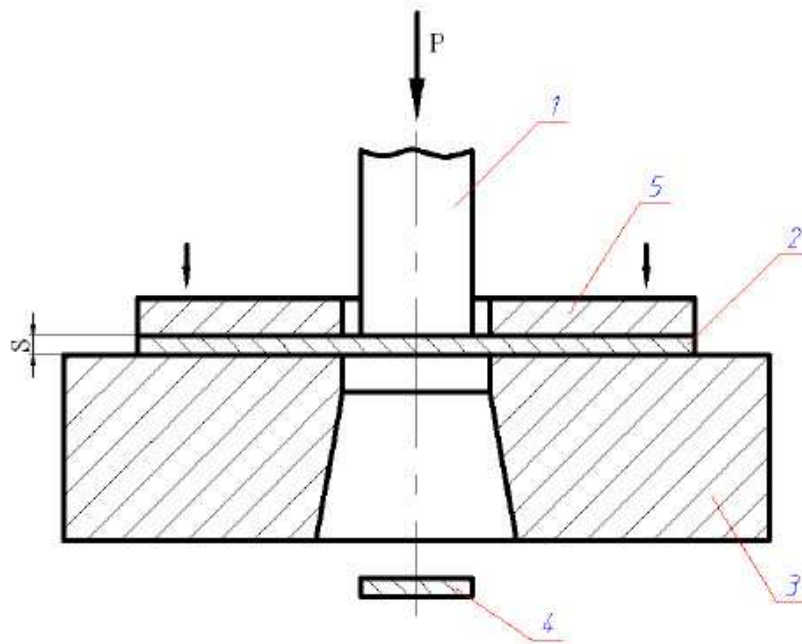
Схема процесу вирубкы (пробивання)
